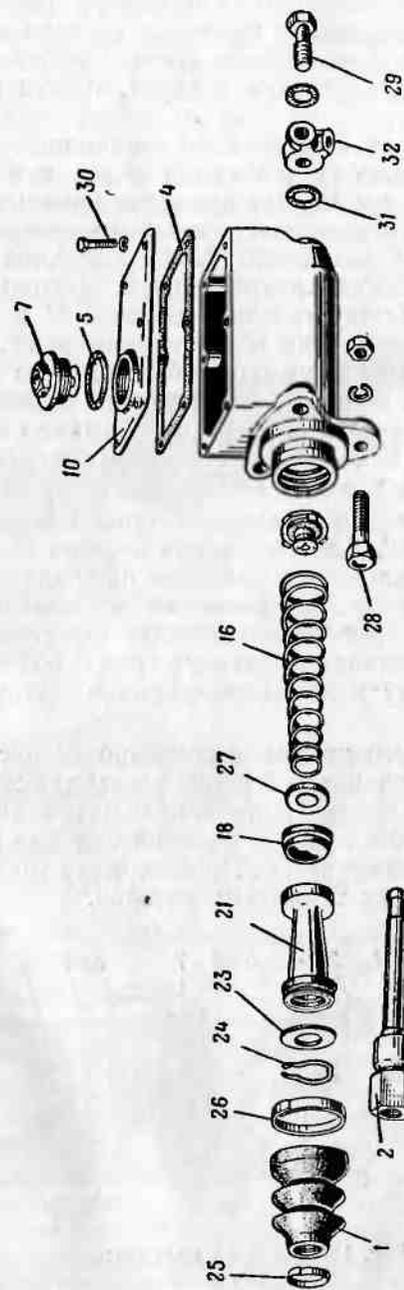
Детали главного цилиндра (обозначение деталей то же, что на рис. 135):
